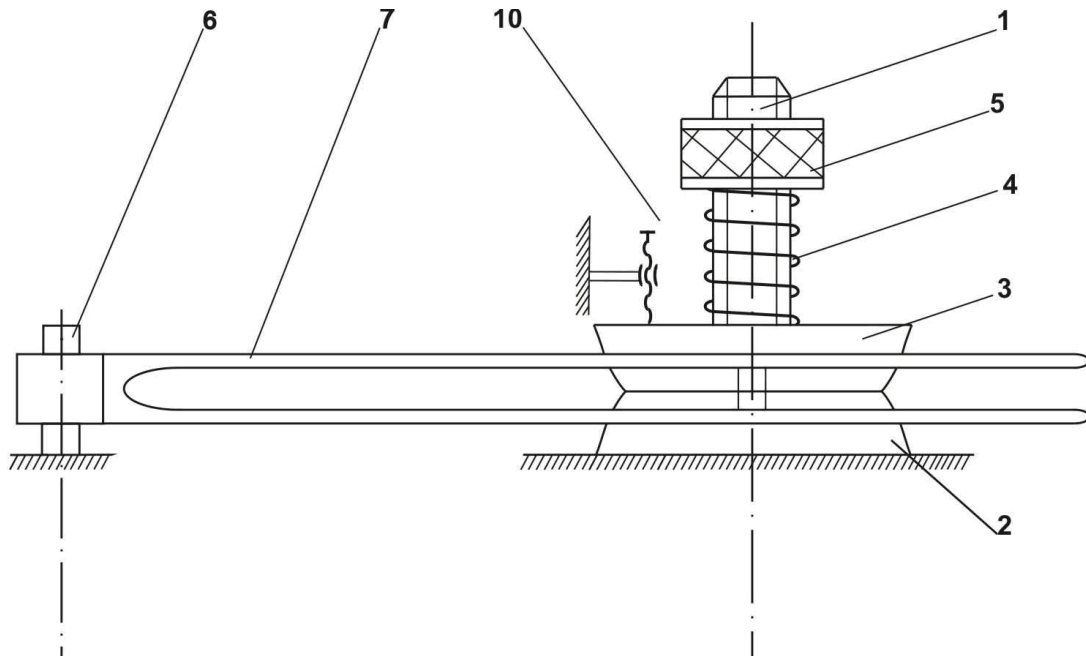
Нитконатягувальний пристрій (вид збоку)
